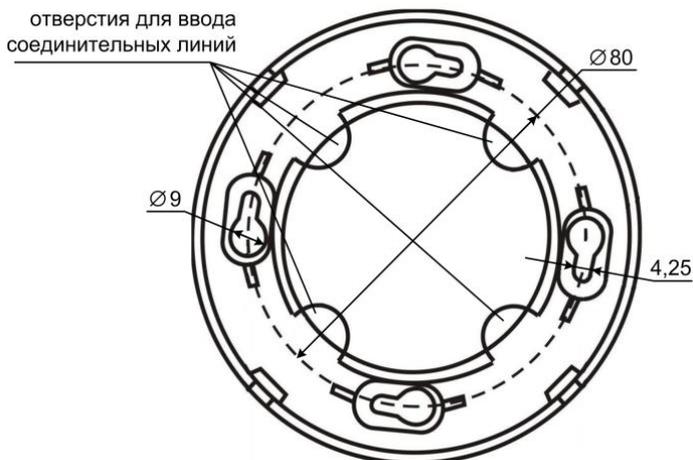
База извещателя. Расположение отверстий для крепления. Присоединительные размеры
